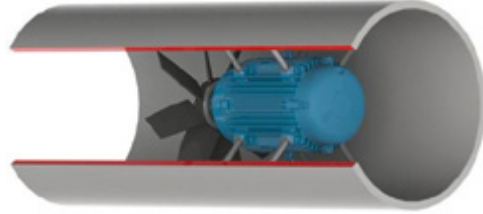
Gövde tabanı destekli flanşlı motorların montaj yöntemi
